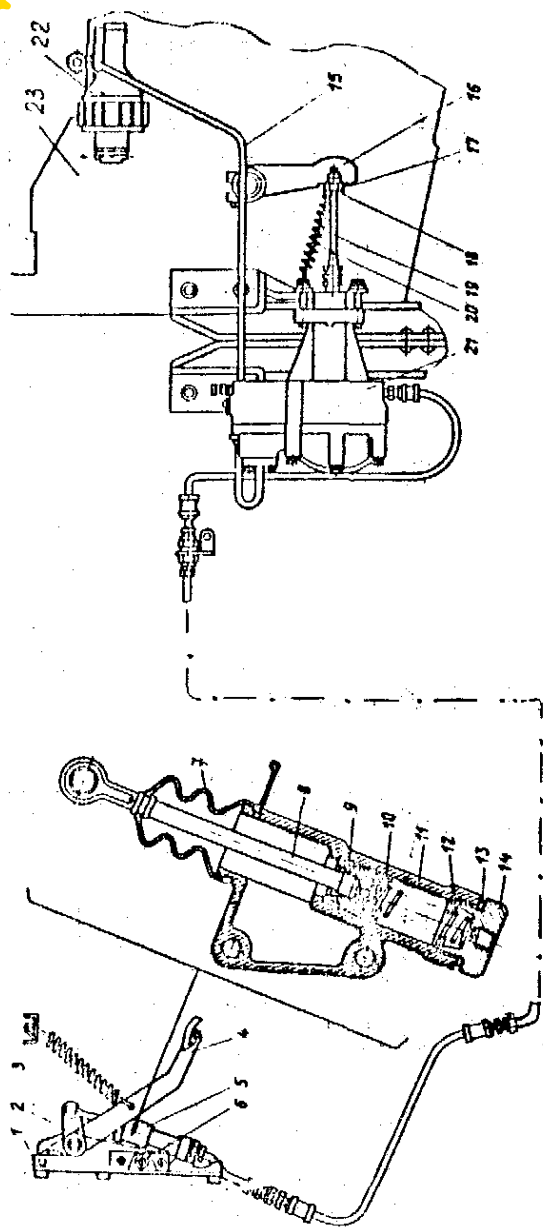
Гідравлічний привод зчеплення з пневматичним підсилювачем: 1 – кронштейн педалі; 2 – важіль штовхача поршня; 3 – відтяжна пружина; 4 – педаль зчеплення; 5 – головний циліндр; 6 – обмежувач ходу педалі; 7 – захисний чохол; 8 – штовхач поршня; 9 – поршень; 10 – манжета поршня; 11 – корпус; 12 – пружина; 13 – ущільнюоче кільце; 14 – пробка; 15 – трубка підводу повітря; 16 – важіль вмикання підсилювача; 17 – сферична гай; 18 – контргайка; 19 – штовхач поршня пневмогідропідсилювача; 20 – зворотна пружина; 21 – пневмогідропідсилювач; 22 – розподільна коробка повітря; 23 – картер зчеплення
